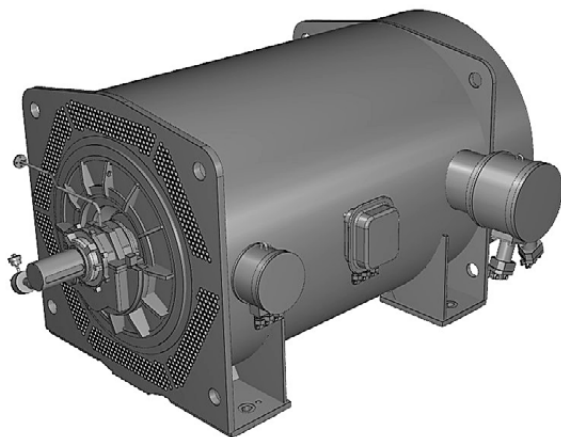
Двигатель 5АЗМВ-6300/10000У2,5
